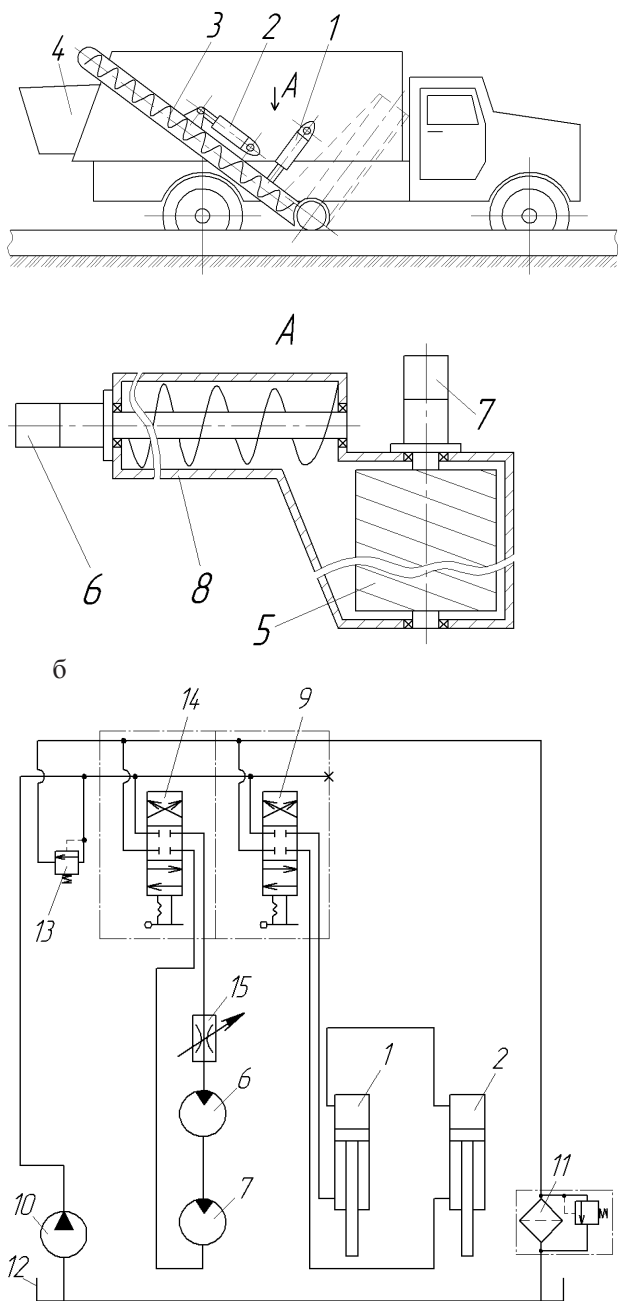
Гідрокінематична схема привода навісного підмітального обладнання сміттєвоза: 1 — гідроциліндр повороту щітки; 2 — гідроциліндр шнека; 3 — шнековий транспортер; 4 — приймальний бункер; 5 — циліндрична щітка; 6 — гідромотор шнекового транспортера; 7 — гідромотор циліндричної щітки; 8 — корпус; 9 — гідророзподільник гідроциліндрів; 10 — гідронасос; 11 — фільтр; 12 — маслобак; 13 — запобіжний клапан; 14 — гідророзподільник гідромоторів; 15 — дросьель
